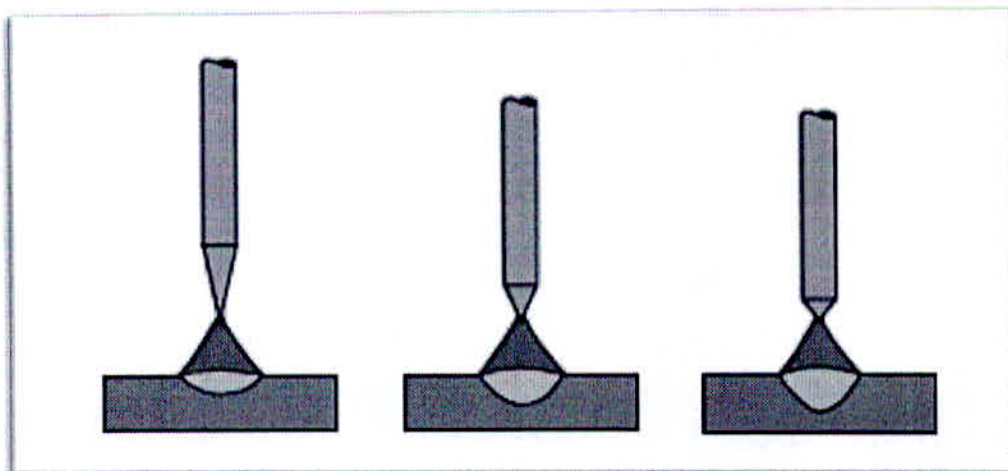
Formatos de afiação de eletrodo de tungstênio para soldagem GTAW
